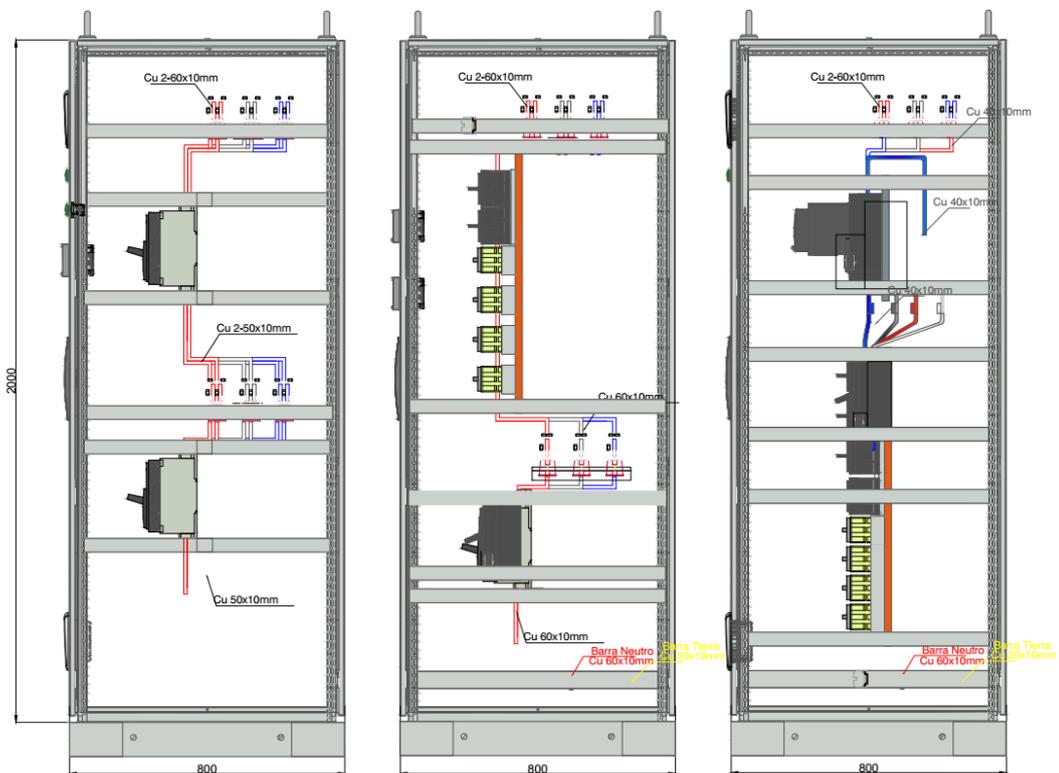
Diseño Mecánico del Tablero en AutoCAD - Vista Perfil.
